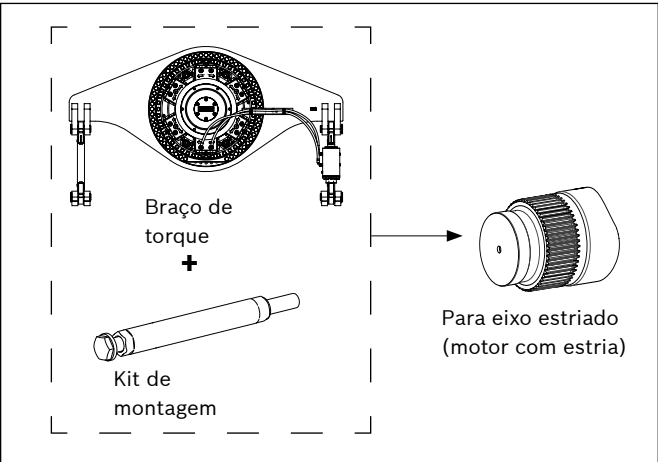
Montagem do braço de torque de duas terminações no eixo estriado
